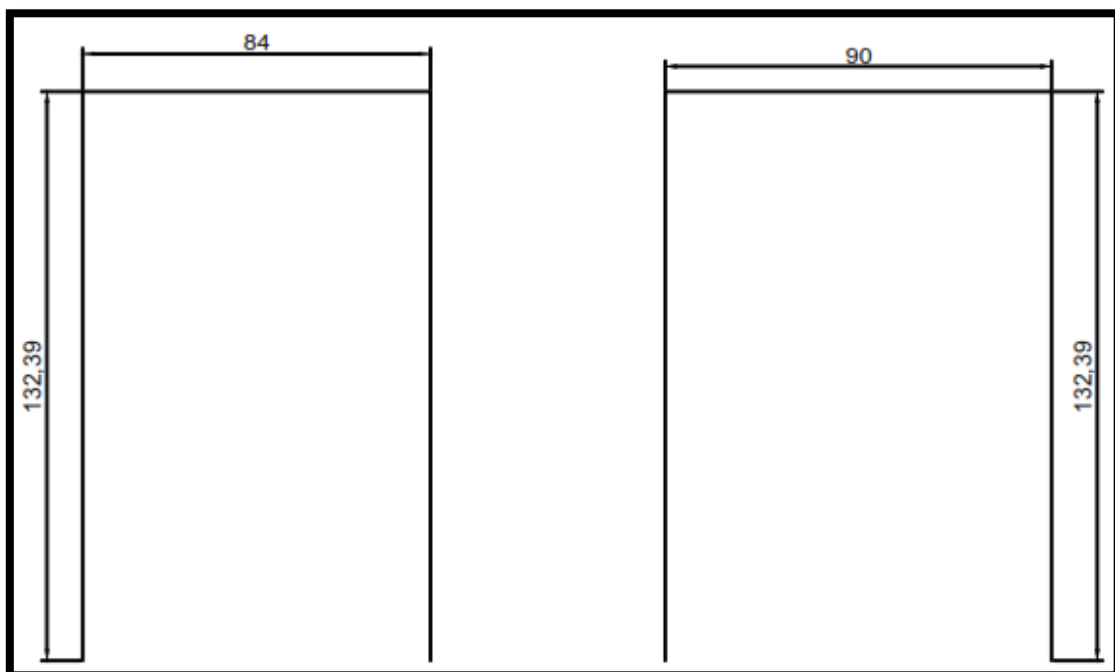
Dimensiones del perfil para el tambor de tostado.
